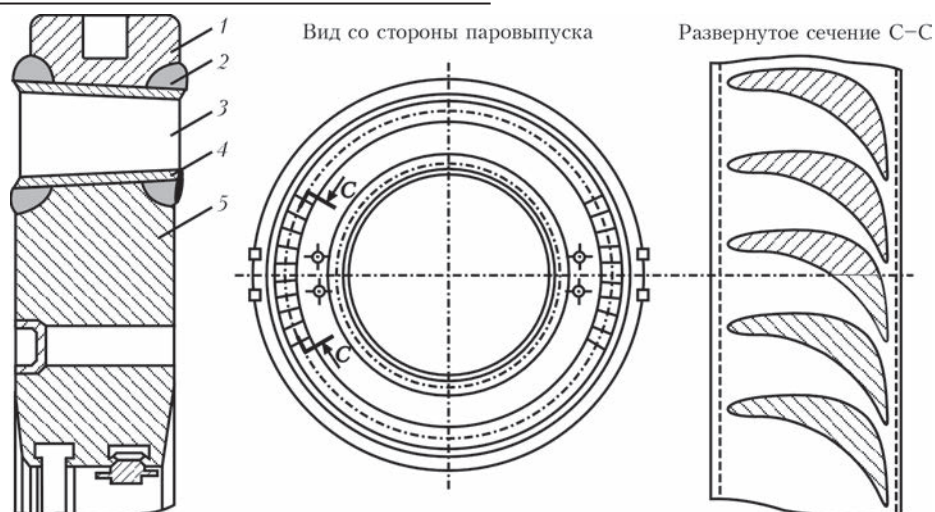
Типовая конструкция сварной диафрагмы паровой турбины: 1 — обод; 2 — верхняя бандажная лента; 3 — направляющие лопатки; 4 — нижняя бандажная лента; 5 — тело
